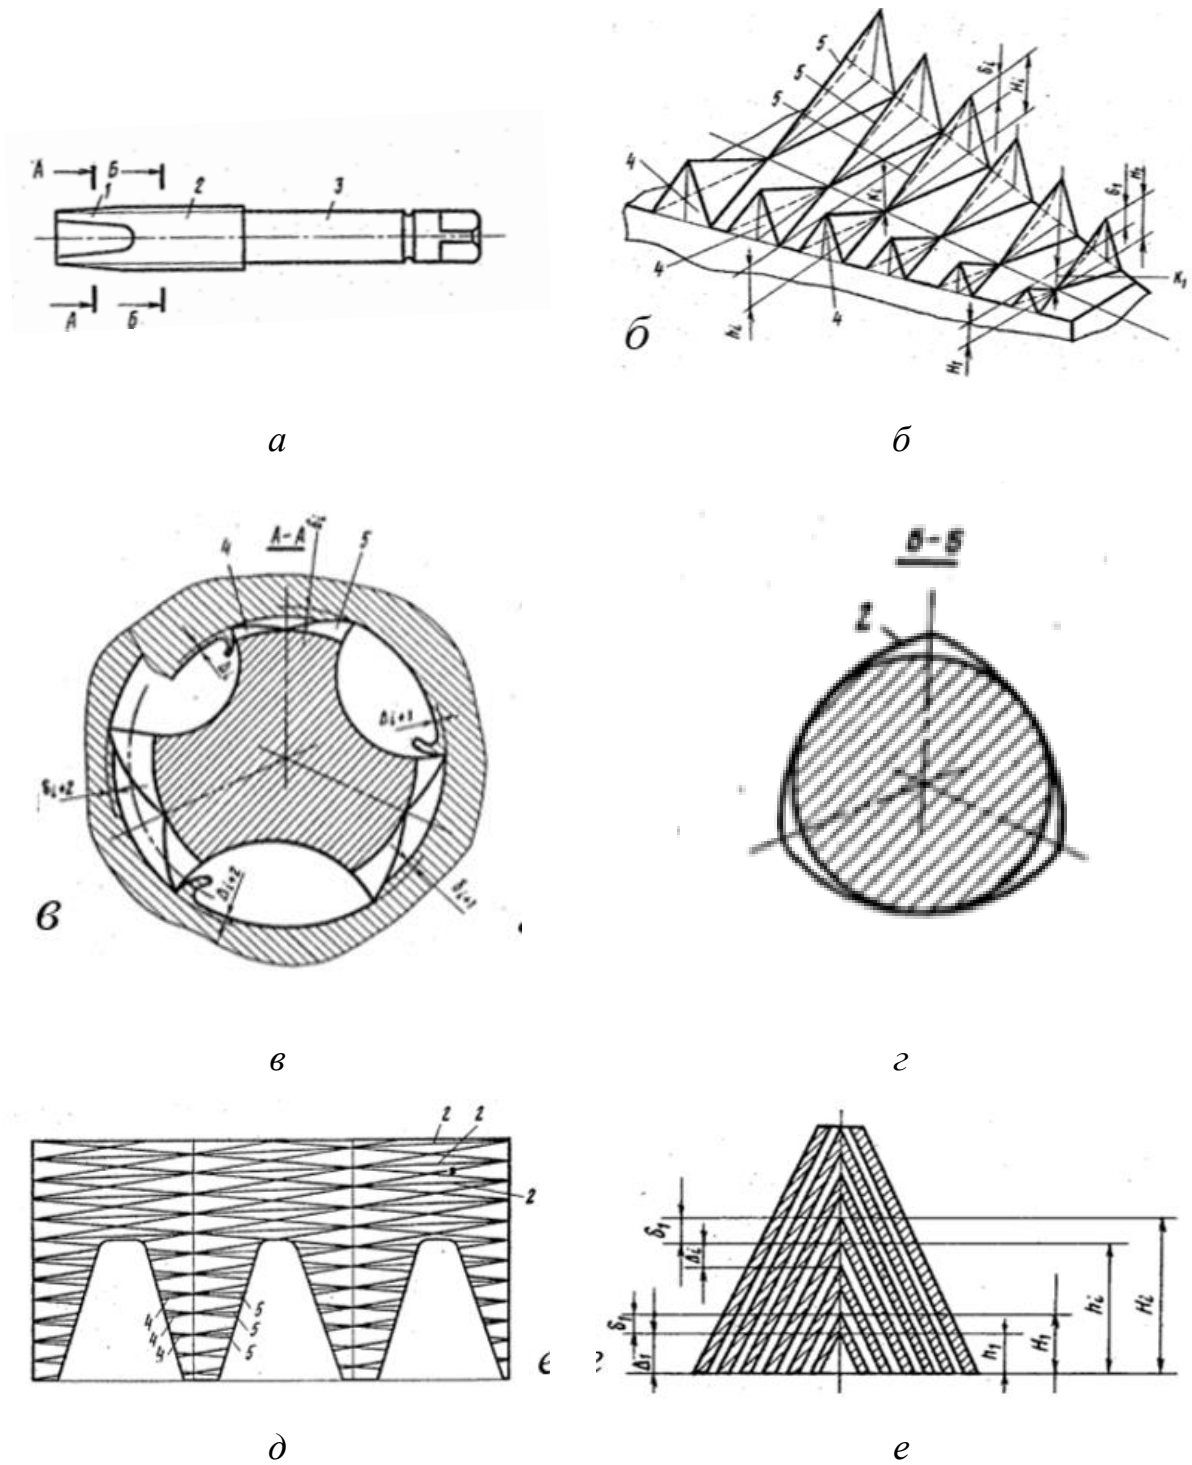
Режуще-деформирующий метчик [65]: *а* – общий вид; *б* – перья заборной части; *в*, *г* – сечения А-А и Б-Б общего вида; *д* – развертка рабочей поверхности; *е* – схема формообразования резьбового профиля
